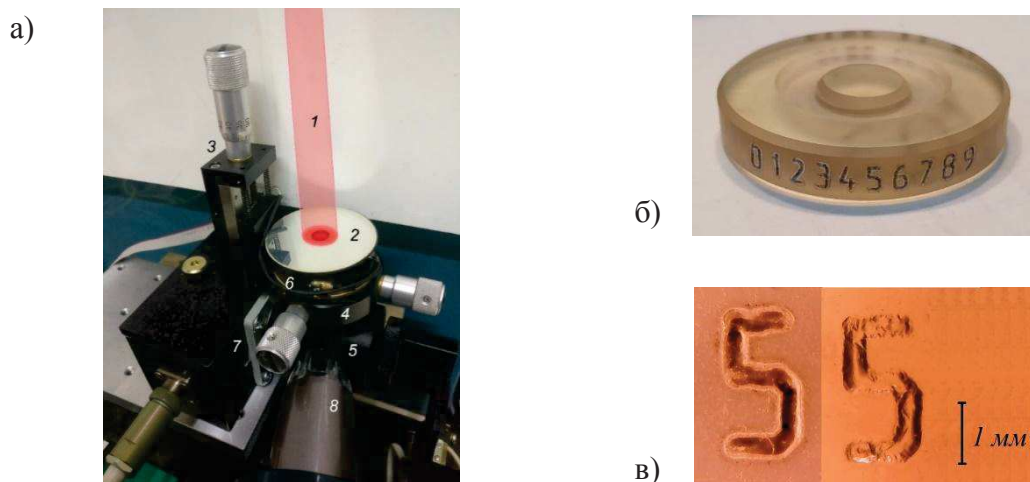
а) Общий вид рабочей зоны установки лазерной гравировки боковой поверхности ситалловой подложки (1 – излучение CO_2 лазера; 2 – зеркало с алюминиевым покрытием; 3,4 – юстировочные устройства; 5 – держатель образцов; 6 – электромеханическое устройство двухкоординатного позиционирования расположенной на нем линзы из ZnSe ; 7 – шаговый двигатель для поворота образцов; 8 – цифровой микроскоп); б) пример лазерной гравировки; в) увеличенное изображение символа до и после химического травления.
